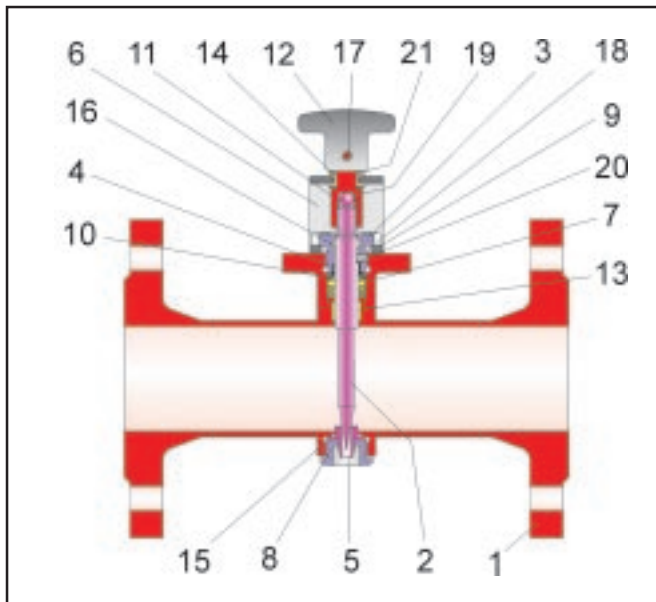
Probenehmerventil BR 27f ( Bauform ab DN 50)
